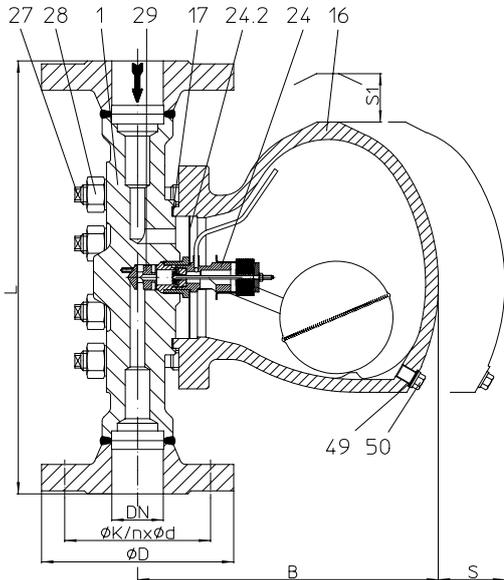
1 mit Flanschen - vertikale Einbaulage
